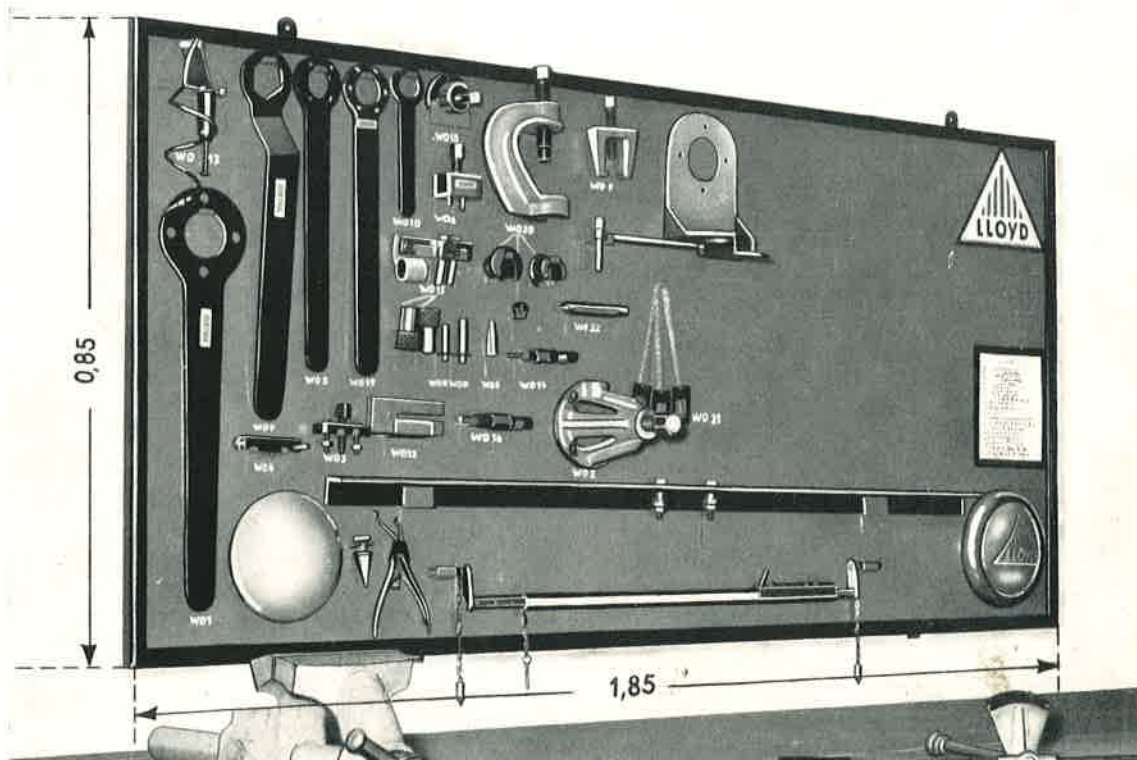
/3: Diese Spezialwerkzeug-Tafel hängt in der KD-Schule des Werkes. Sie sollte in keiner Werkstatt fehlen. Für weitere Spezialwerkzeuge ist Platz auf der rechten Tafel-Hälfte.
